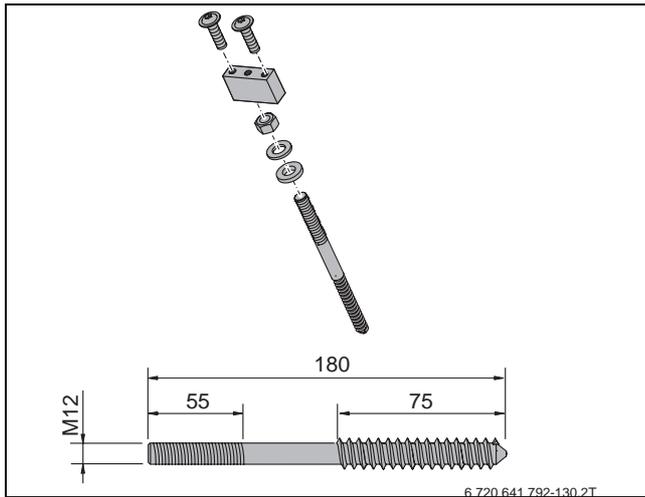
Vite prigioniera per il collegamento da tetto di piastre ondulate o lamiera SKS4.0 (misure in mm)
